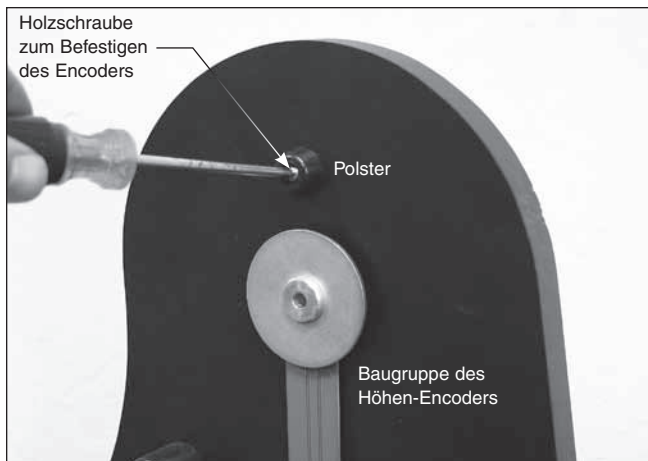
Schrauben Sie das Polster mit einer der Holzschrauben zum Befestigen des Encoders in die Pilotbohrung über der Baugruppe des Höhen-Encoders.
